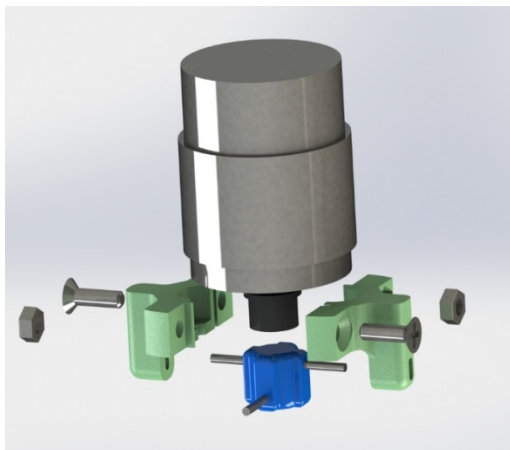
Vista explodida da ligação entre o motor e o cardan
